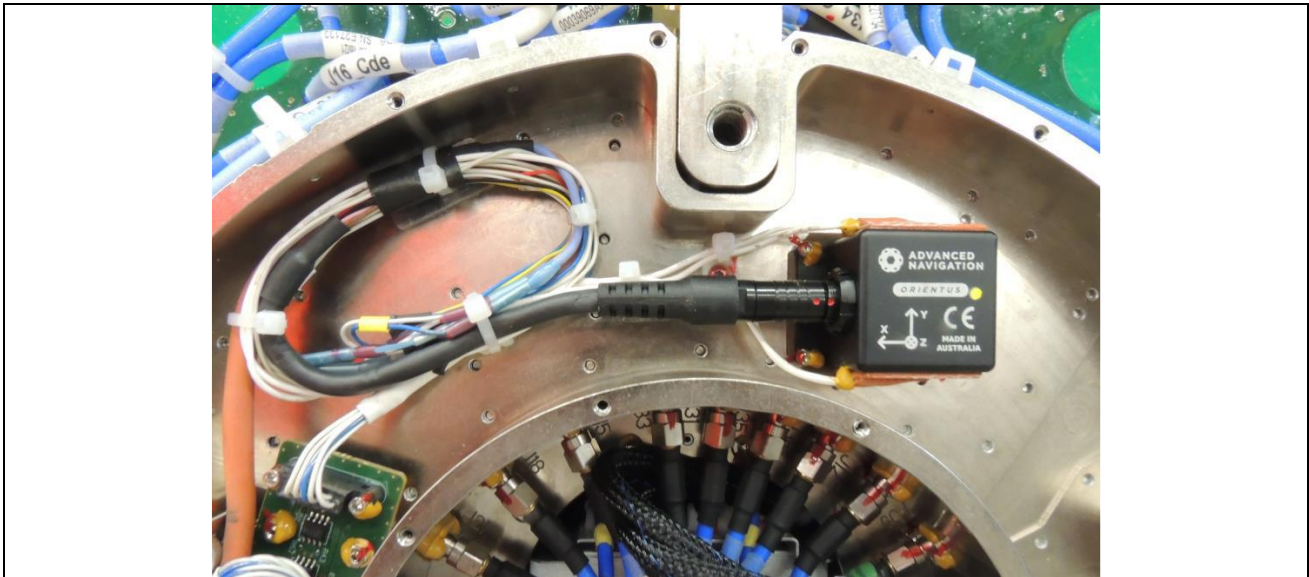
Robustification des patches chauffants, points de Scotch-Weld
